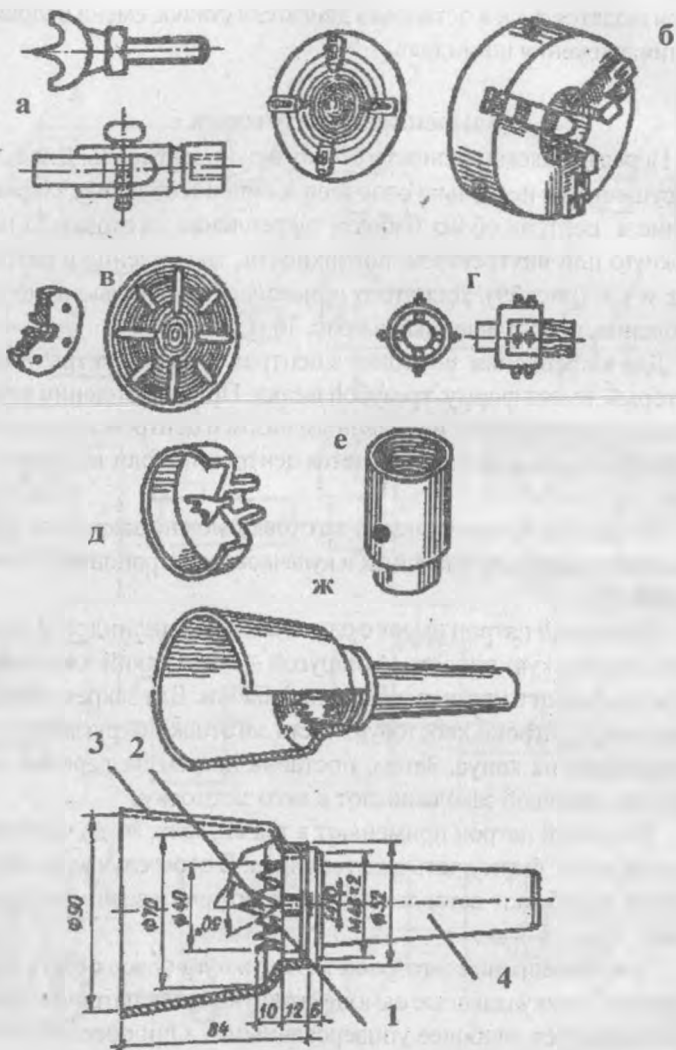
Приспособления для закрепления и обработки заготовок на станке:
